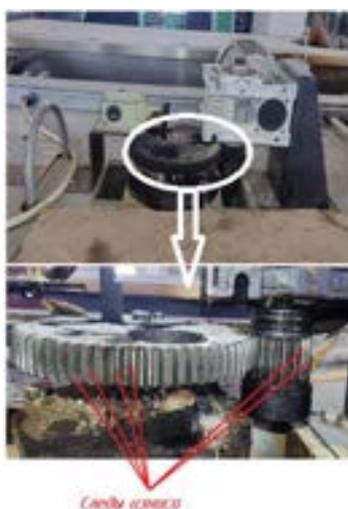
Износ зубьев зубчатой передачи механизма вращения стеллажной тележки
